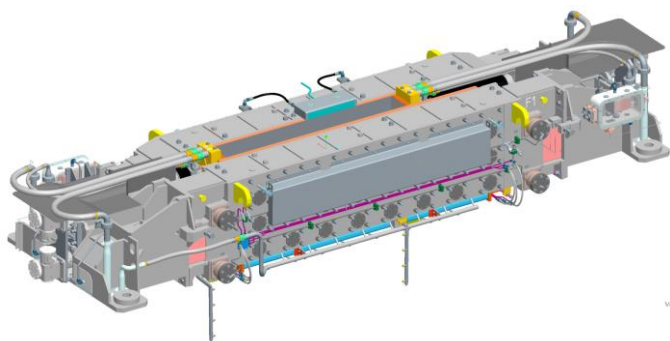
Кристаллизатор машины непрерывного литья заготовок
